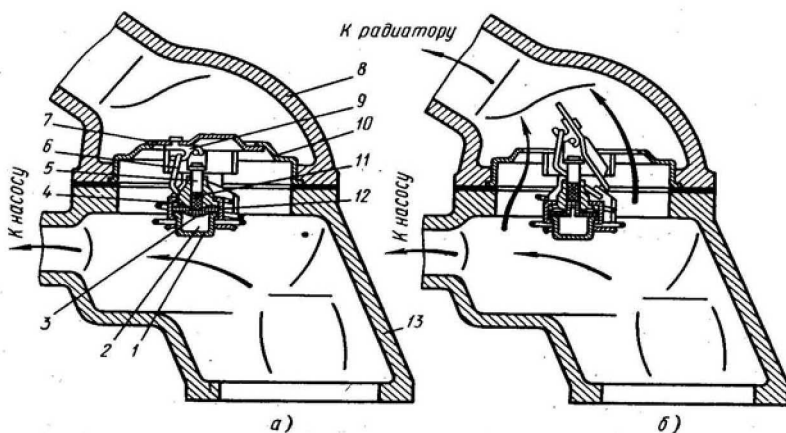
Схема работы термостата: а – клапан закрыт; б – клапан открыт; 1 – термосиловой элемент; 2 – наполнитель; 3 – мембрана; 4 – втулка; 5 – шток; 6 – возвратная пружина; 7 – клапан термостата; 8 – верхний патрубок корпуса; 9 – коромысло клапана; 10 – фланец термостата; 11 – буфер; 12 – рант; 13 – корпус термостата
